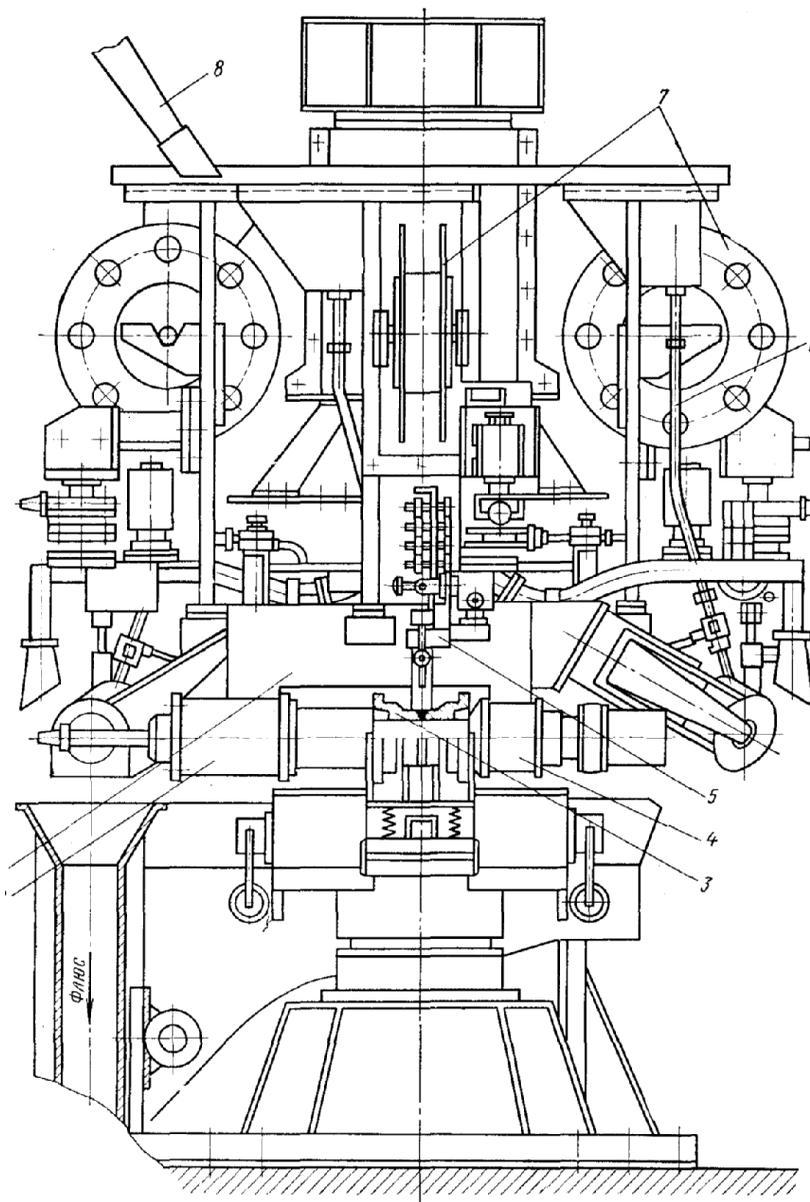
Станок-автомат роторного типа для сборки и сварки катков трактора
